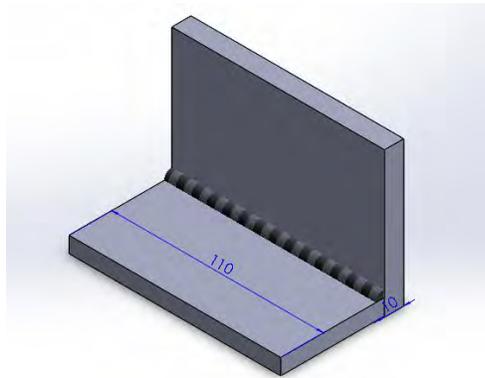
Forma una soldadura en ángulo sencilla
